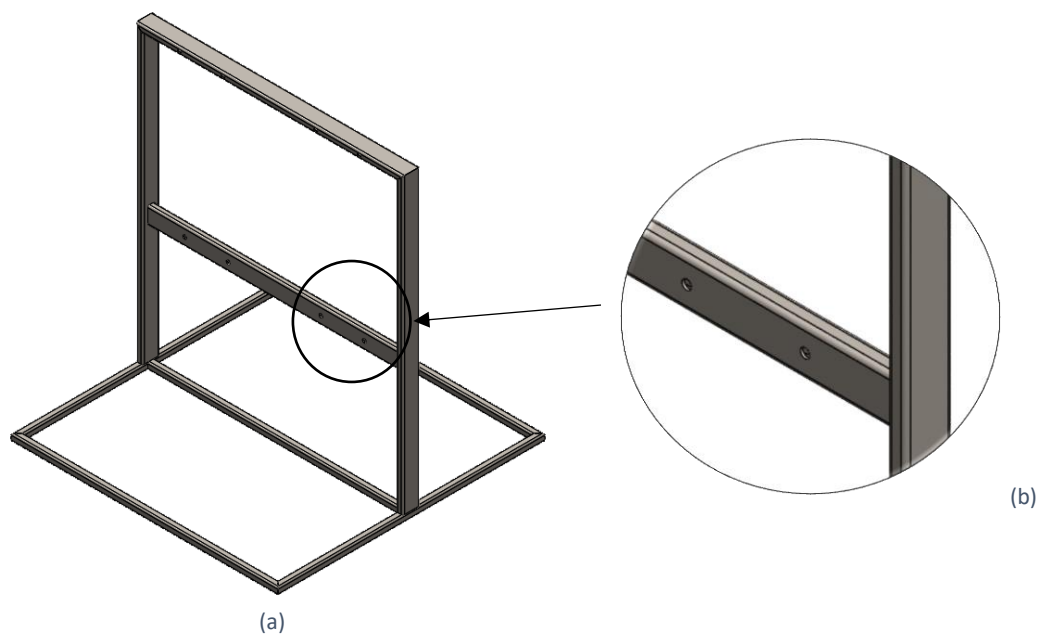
Construção da estrutura metálica: (a) montagem das duas bases, horizontal e vertical e (b) pormenor dos furos existentes na estrutura para acoplar tubos de paletização.
